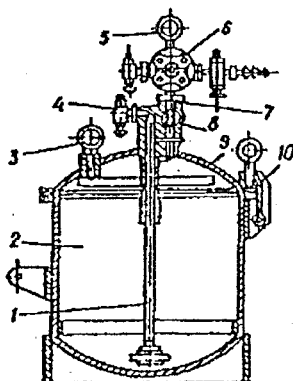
Фарбонагнітальний бак СО-13А: 1 - відбивач; 2 - бак; 3,5 - манометри; 4 - триходовий кран; 6 - редуктор; 7 - поворотний клапан; 8 - розподільник; 9 - кришка; 10 - скоба
